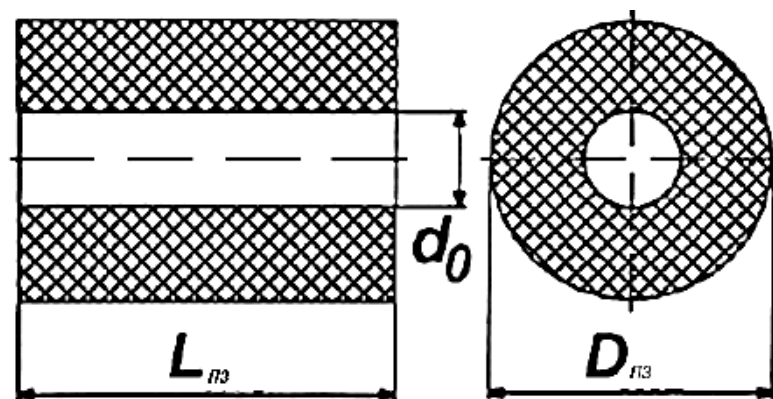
Одношашковий трубчастий циліндричний заряд
